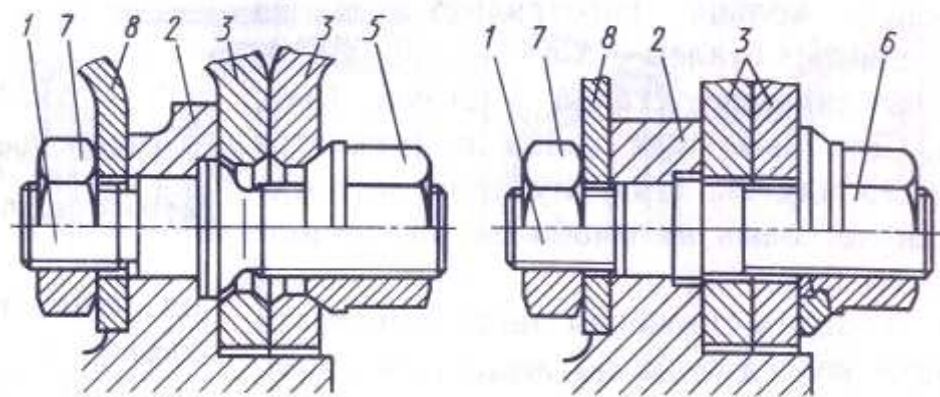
Крепления по стандарту ИСО 4107-79 с центрированием диска по центральному отверстию и закреплением обоих дисков гайками с завальцованной шайбой:
